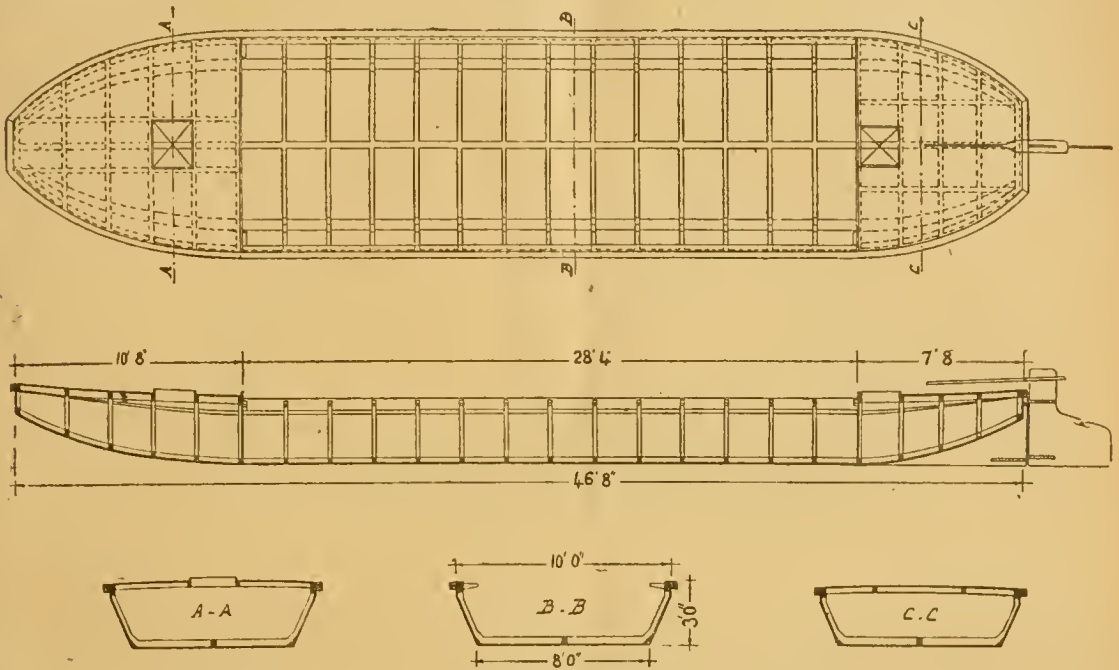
Plan, élévation et coupes d'un chaland hollandais, système Boon, pour le transport des cendres et des vases.
